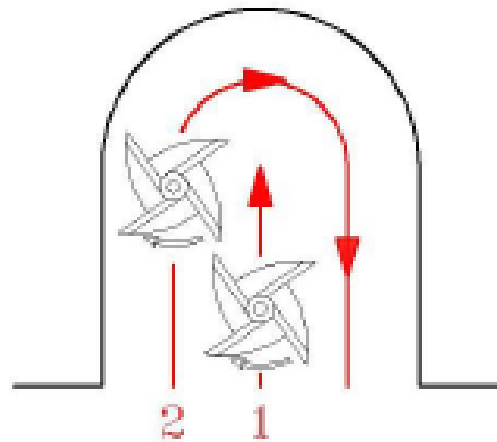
Фрезерування за контуром паза з попереднім центральним проходом
